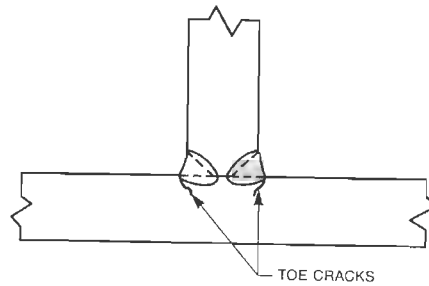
Grieta en la pierna de la soldadura
